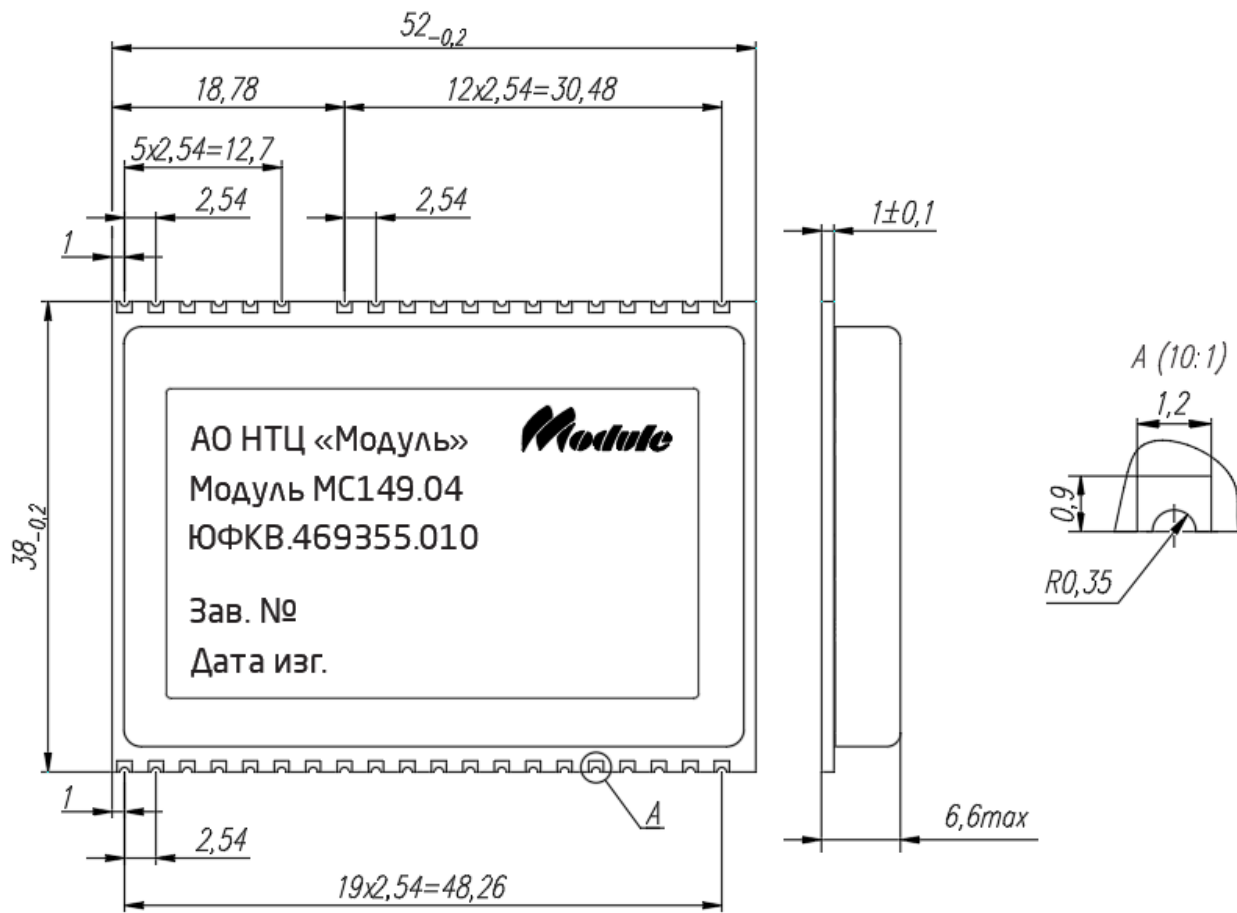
Габаритные и присоединительные размеры Модуля
